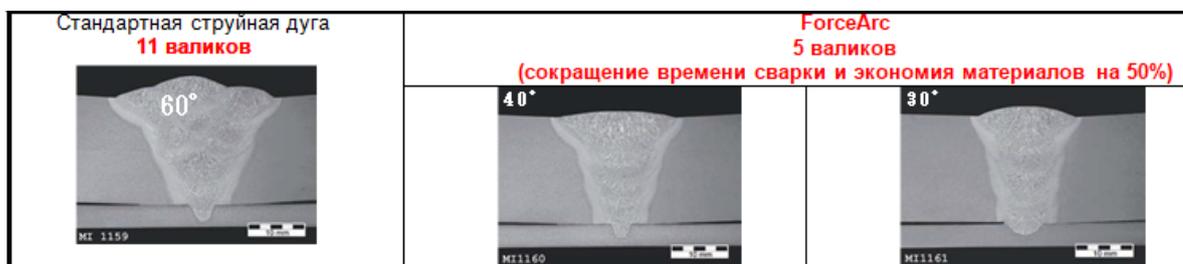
Сравнение методов ForceArc и стандартной сварки струйной дугой
